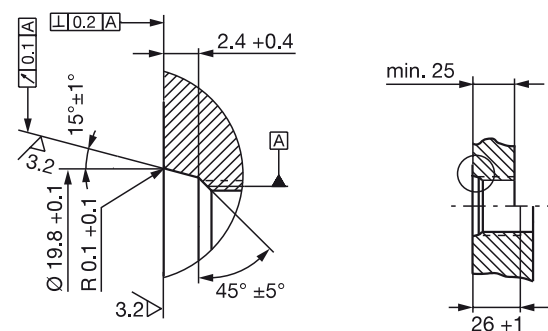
Einschraubloch M18×1.5 nach ISO 6149 O-Ring 15.4×2.1
